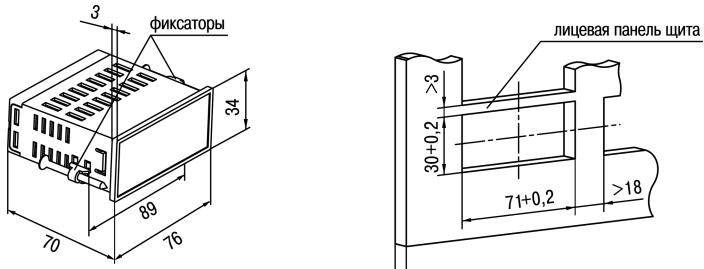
Габаритные размеры корпуса Щ3
